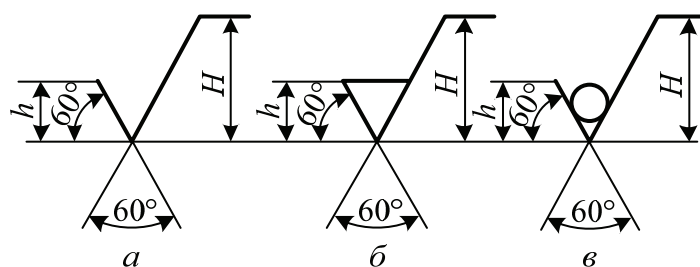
Знаки для обозначения шероховатости на чертежах
